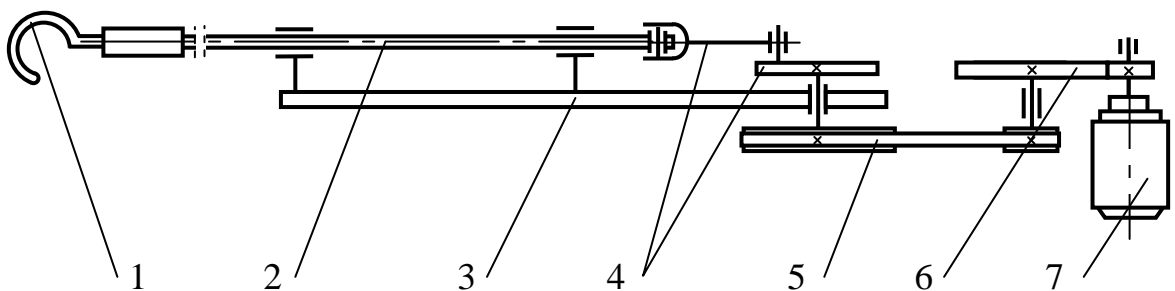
Схема ручних струшувачів OEG-8 і OEG-12 (Німеччина): 1 – гак-захват; 2 – штанга; 3 – остов; 4 – кривошипно-шатунний механізм; 5, 6 – пасова і зубчаста передачі; 7 – електродвигун
